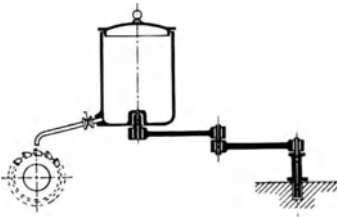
Ungünstige Zuführung des Kühlmittels.
